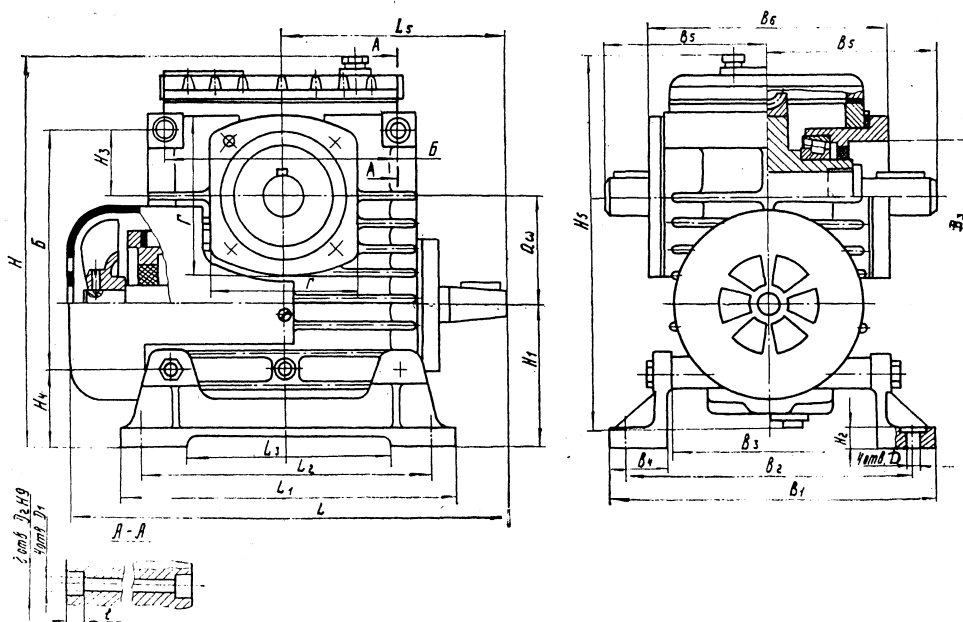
П7 Габаритные и присоединительные размеры редуктора Ч-80
